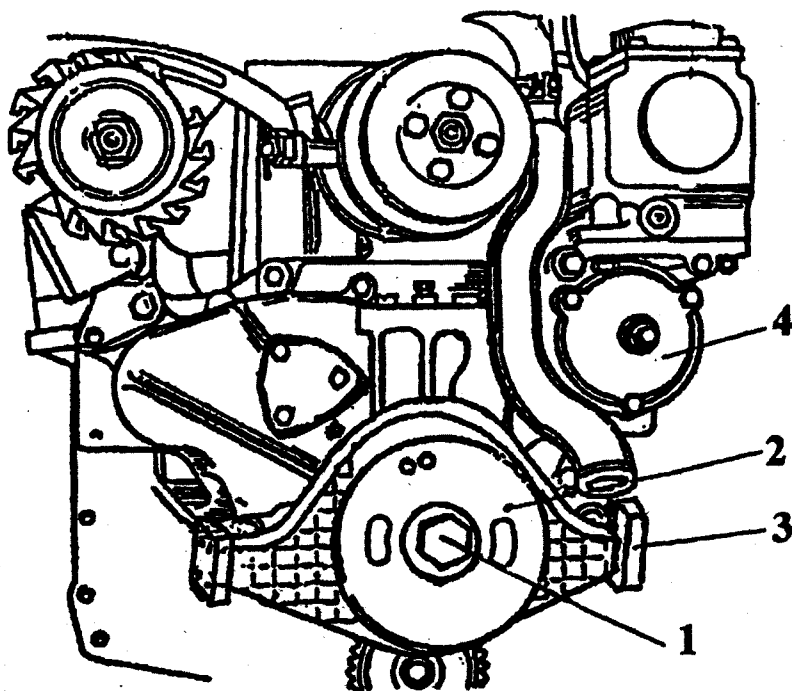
Снятие передней опоры двигателя, шкива коленчатого вала и лючка
